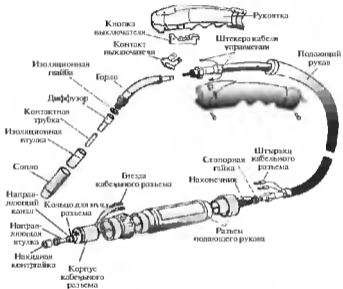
Устройство горелки для газоплазменной сварки
